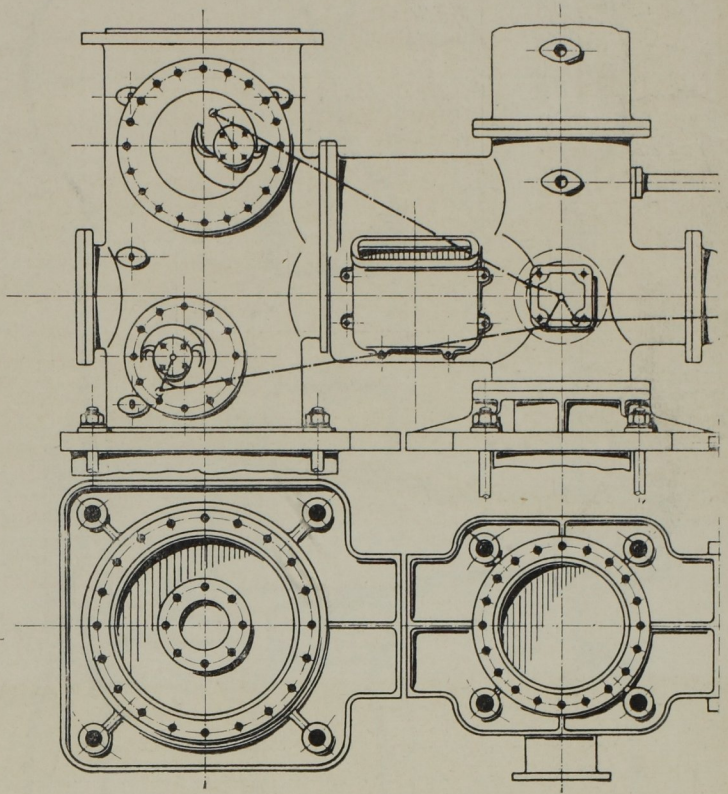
Seitenansicht und Grundriss einer Pumpe.
